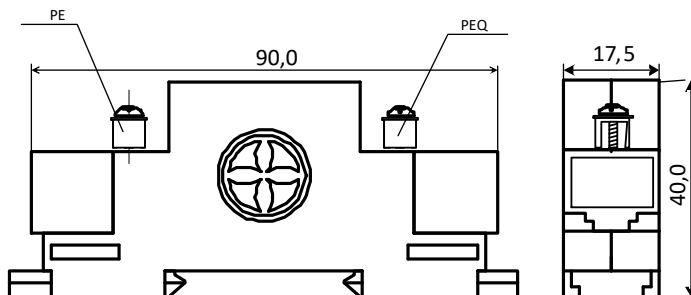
Габаритные размеры устройства Commeng Cat5P
